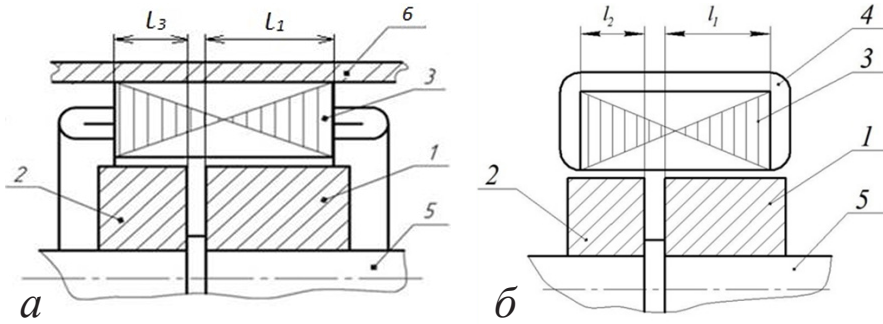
Продольное сечение электромеханической части БДПТ с обычной ЯО (а) и с тороидальной ЯО (б): 1 – основной индуктор; 2 – дополнительный индуктор; 3 – якорь; 4 – катушка ЯО; 5 – вал; 6 – корпус
